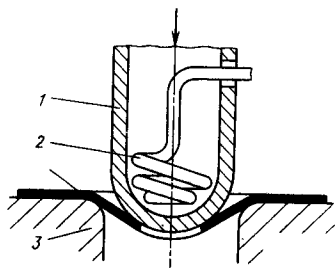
Схема штампа для отбортовки отверстий в листовых заготовках: 1 — пуансон; 2 — нагреватель; 3 — заготовка; 4 — матрица
